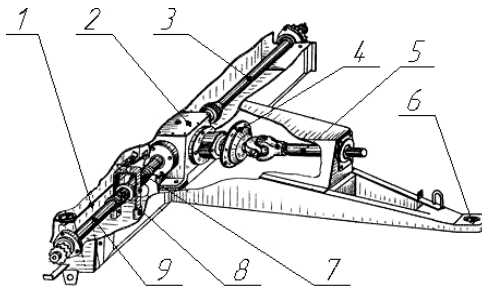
Схема лобовины: 1 – трос; 2 – редуктор конический; 3 – вал привода вальцов; 4 – муфта предохранительная; 5 – вал привода; 6 – петля; 7 – муфта кулачковая; 8 – пружина; 9 – вал привода механизма прессования и подборщика
